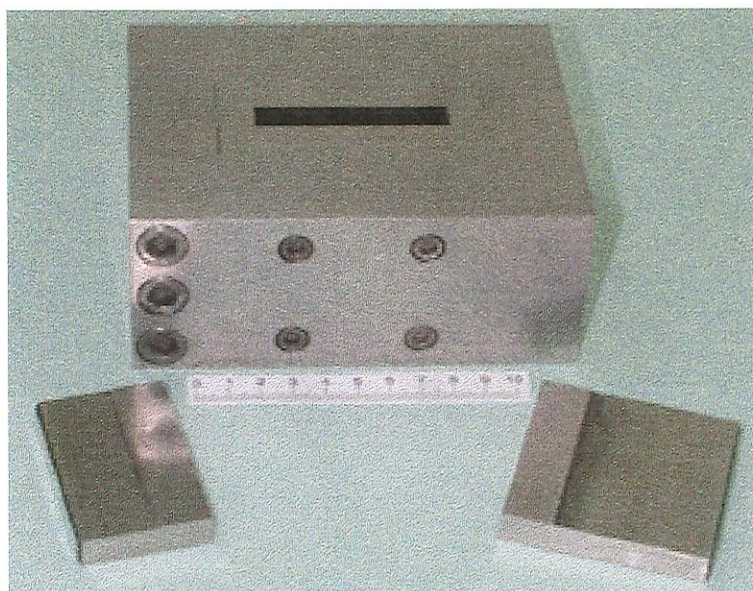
Componentes do molde de compactação dos corpos de prova
